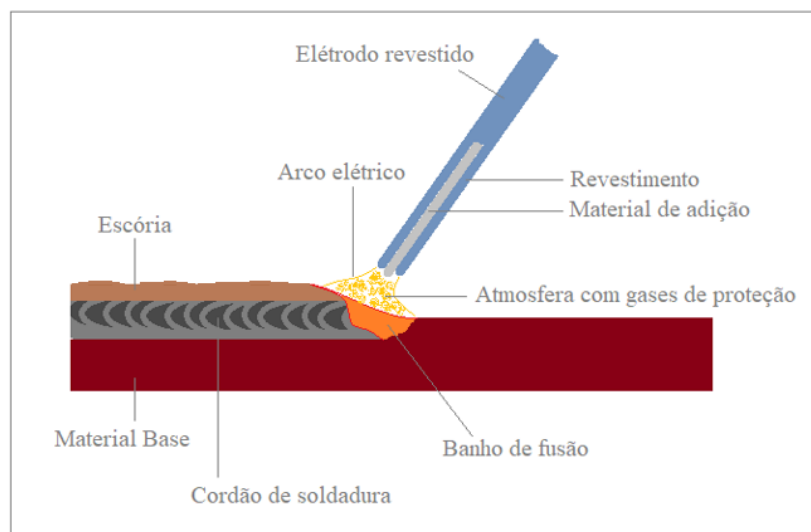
Soldadura MMA, eletrodo revestido – [10] Imagem adaptada
